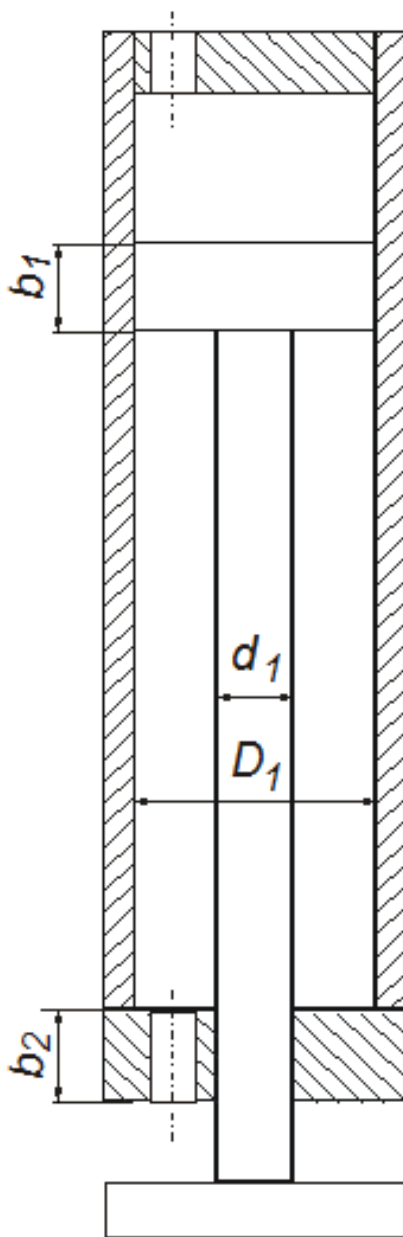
Розрахункова схема пневмоциліндра
